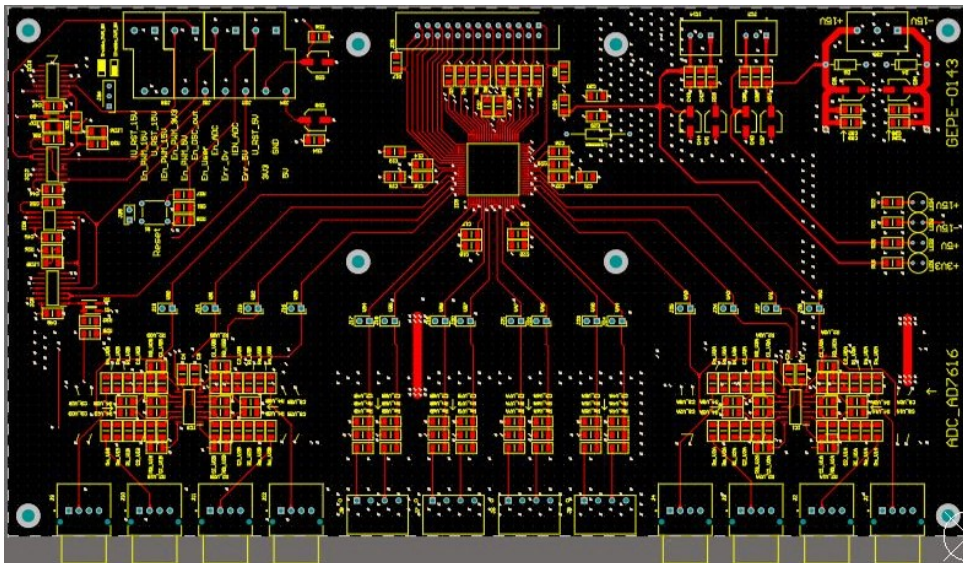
Primeira camada de sinal do ADC externo no Altium PCB Designer.
